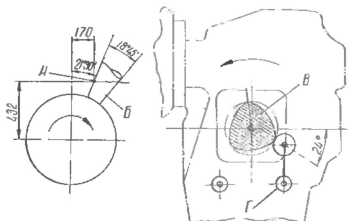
Положение лопасти винта при регулировке выстрела левого пулемета ШКАС (вид против полета) и положение кулачковой шайбы (вид с левого борта на левый синхронизатор).
